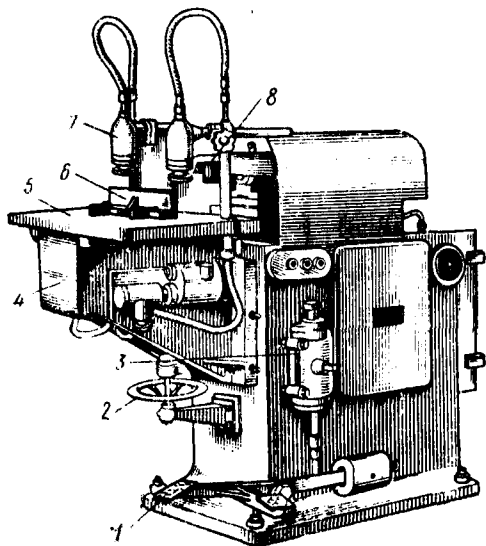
Сверлильно-пазовальный станок СВПГ-2
